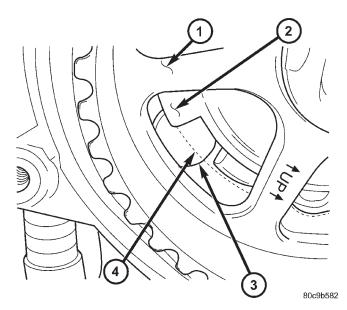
CARA DEL SENSOR DE CMP EN LA RUEDA DE DIRECCION - 2.4L
